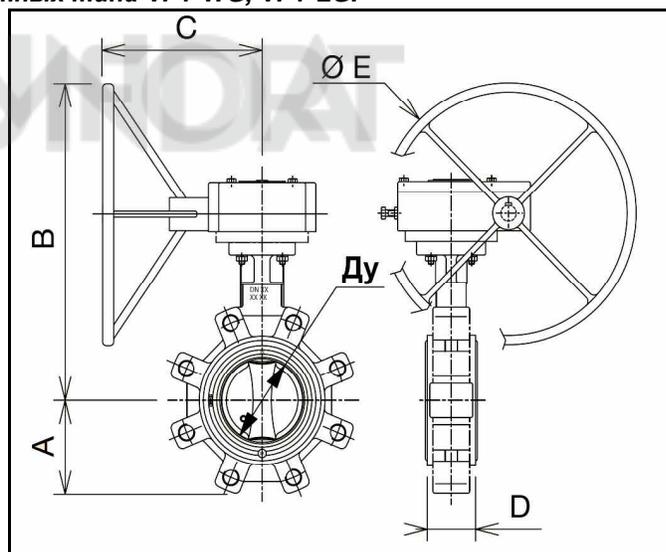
Габаритные и присоединительные размеры затворов дисковых поворотных типа VFY-LG с отверстиями под болты
